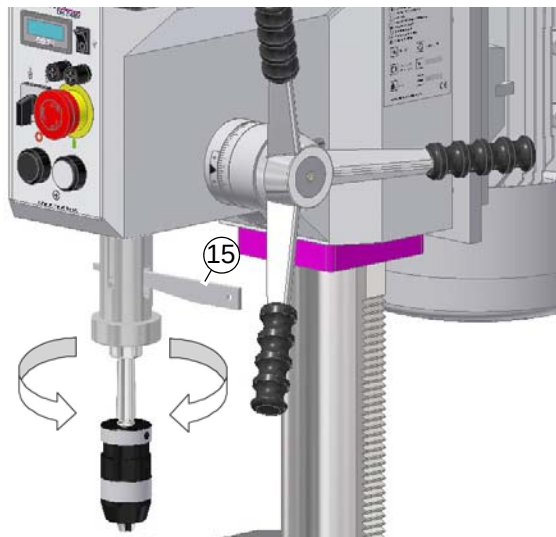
Bedienelemente DH24BV - Werkzeugentnahme
